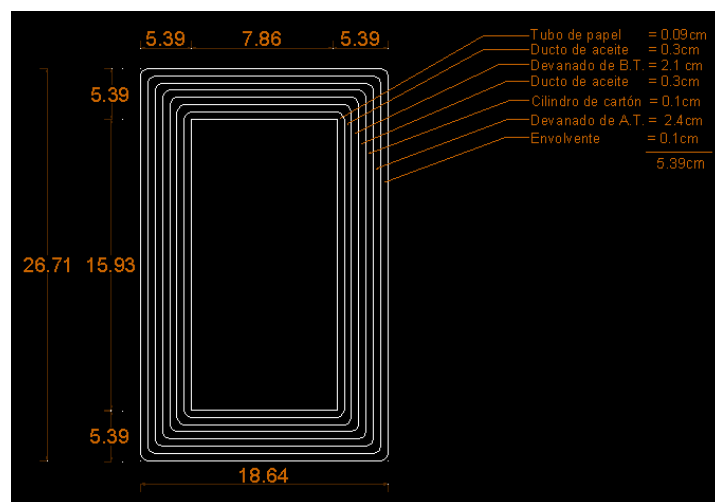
Dimensiones geométricas de la vista superior del conjunto núcleo-devanados.
